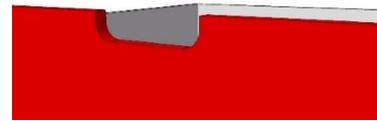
DETALLES TIRADOR CAJÓN CAJONERA
